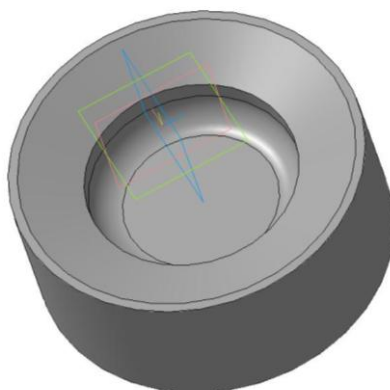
Поковка "Заглушка" – с уклонами на внутренней поверхности
